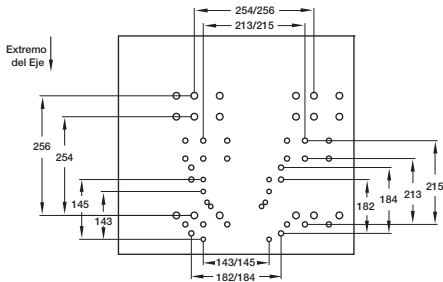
Posiciones de Montaje del Motor según el Tamaño del Bastidor del Motor
